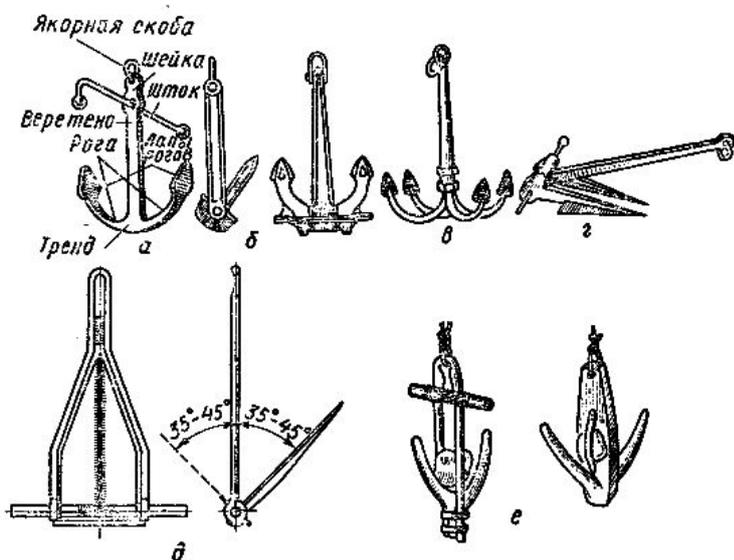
Якоря а — адмиралтейский; б — Холла; в — четырехлапый; г — Матросова, д — четырехлапый сварной Курбатова; е — самодельные из дерева
